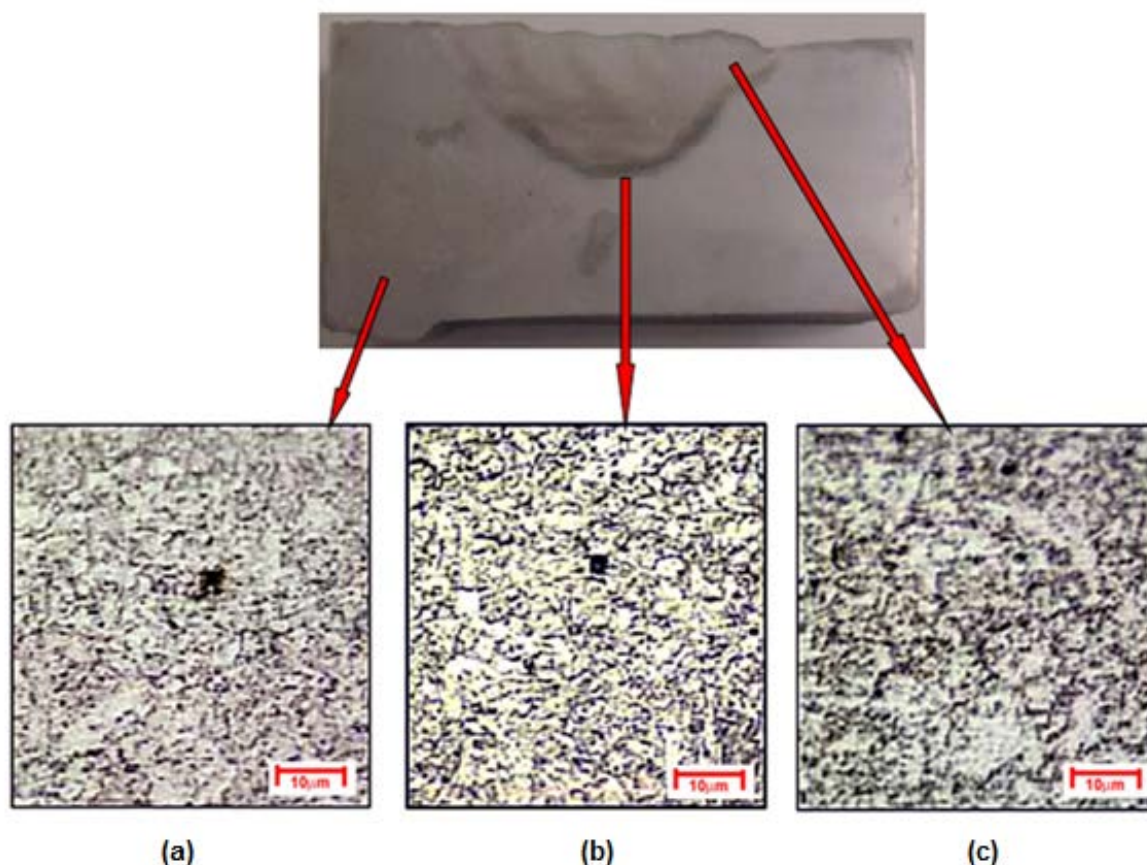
Soldagem com eletrodo revestido - CP do reparo: (a) metal de base (1000x) (b) ZTA (1000x) e (c) metal de solda (1000x).
